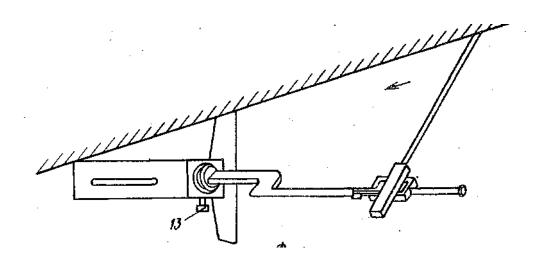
б - Устройство для сварки наклонным электродом
